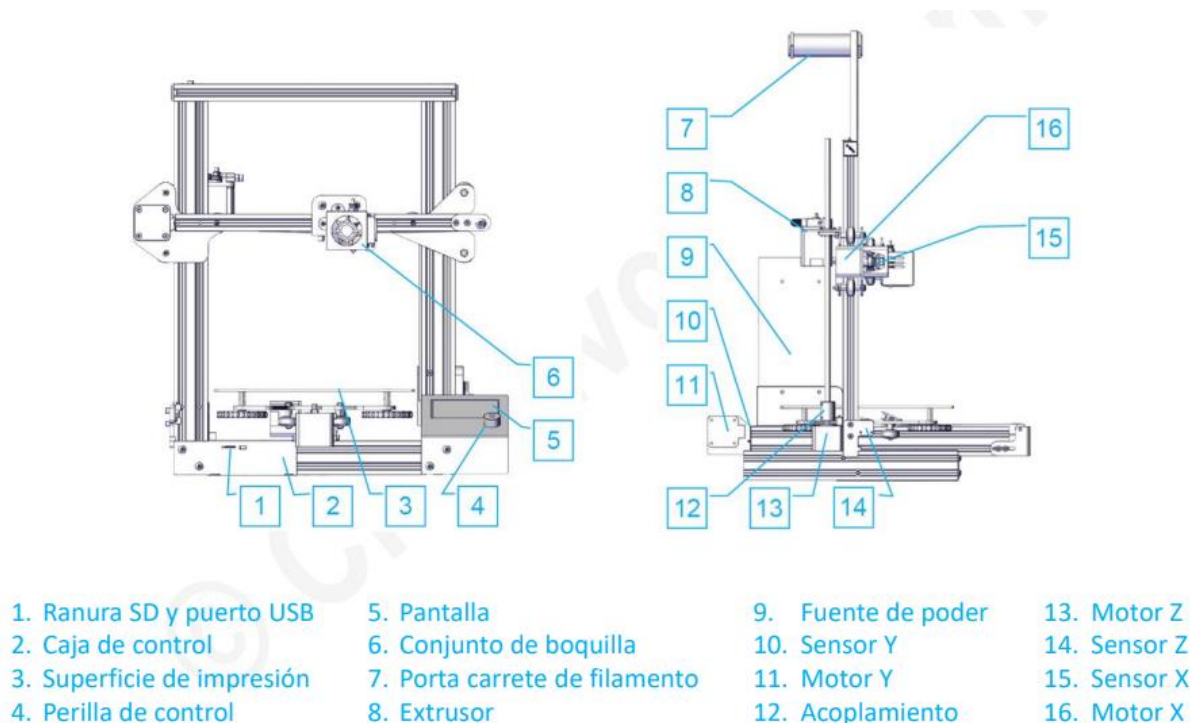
Elementos principales Impresora Ender 3 pro. Fuente [11]
